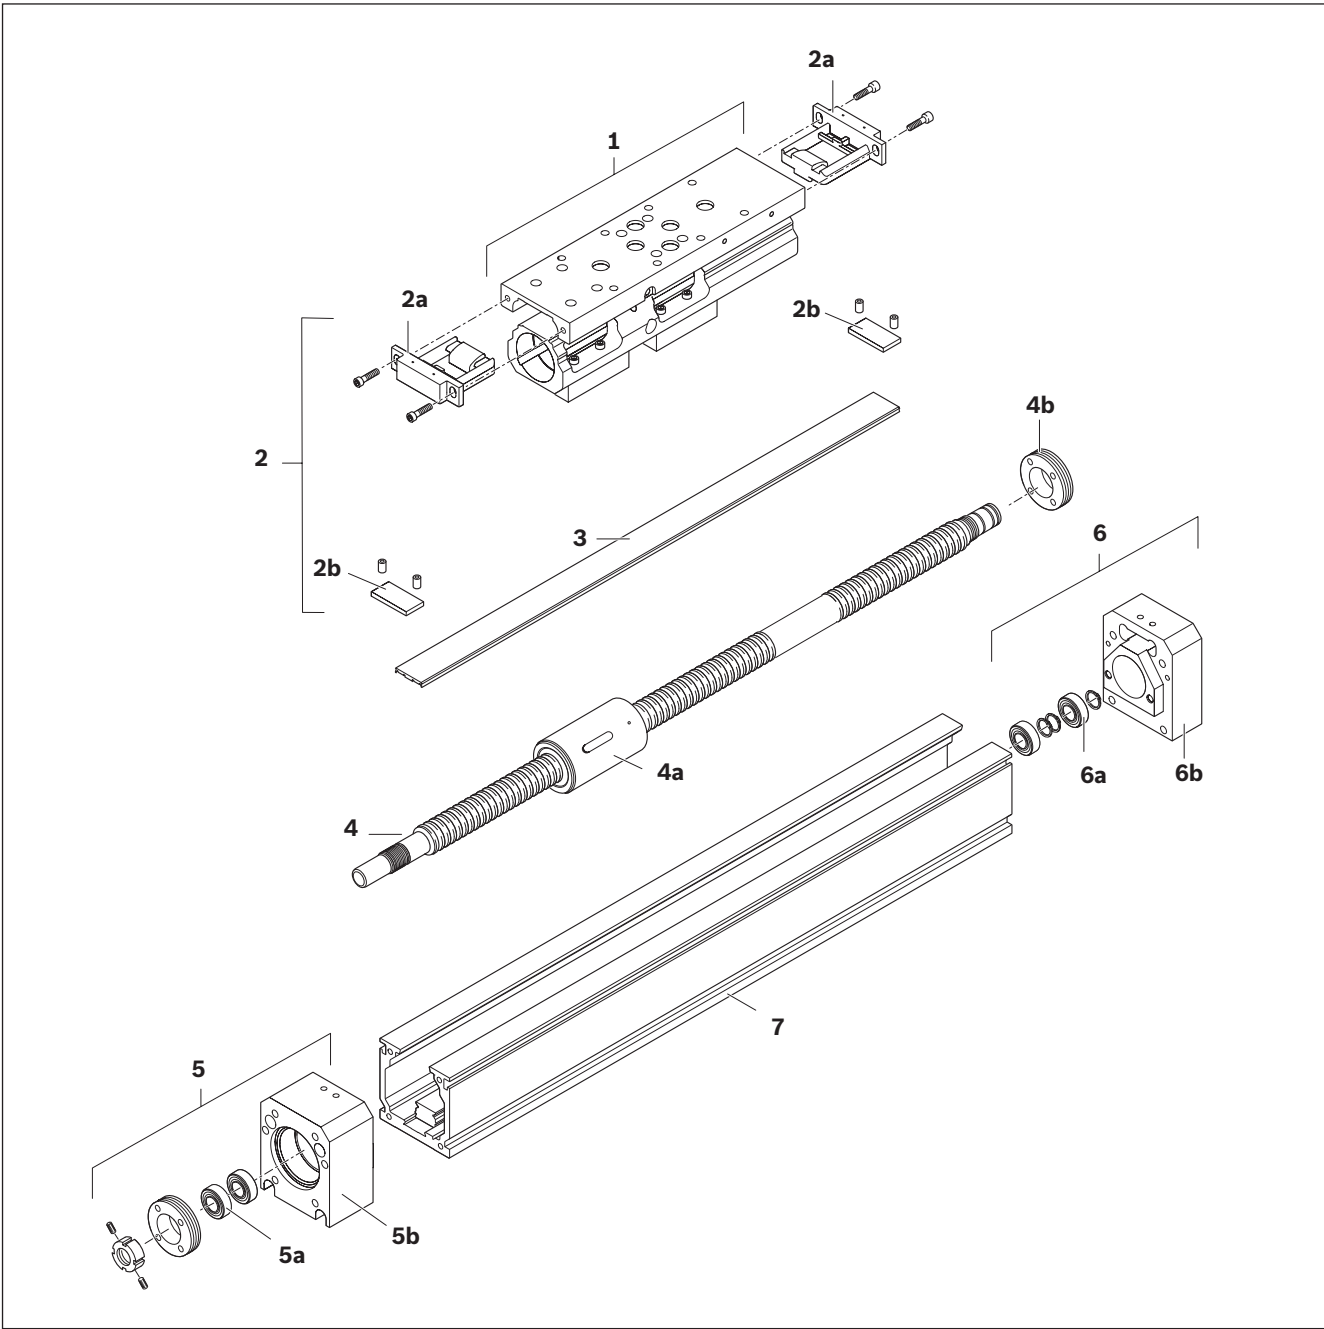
Vue d'ensemble MKK-040-NN-3
